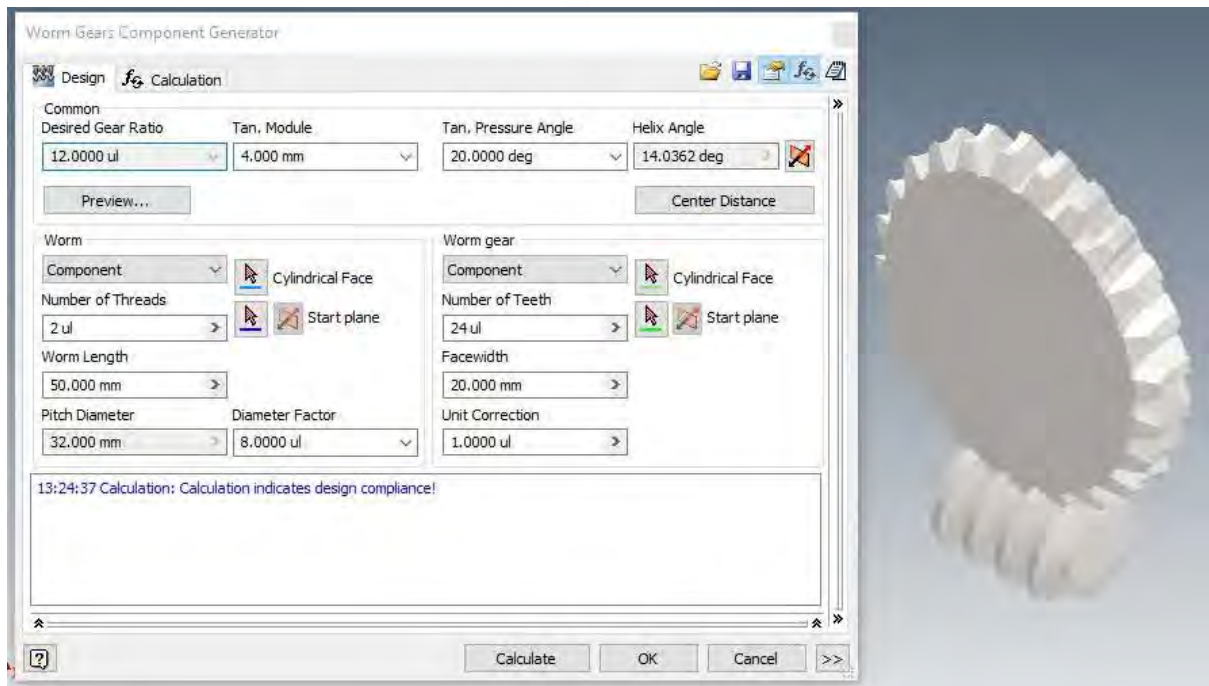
Diseño de corona y tornillo sin fin : Dimensiones
